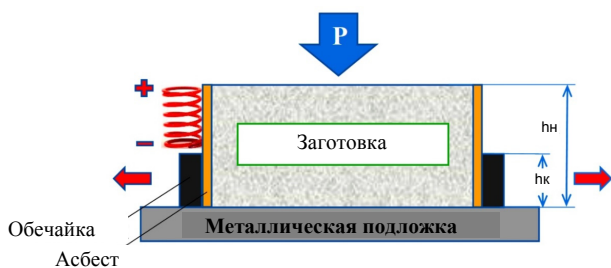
Схема заготовки перед свободным СВС-сжатием
